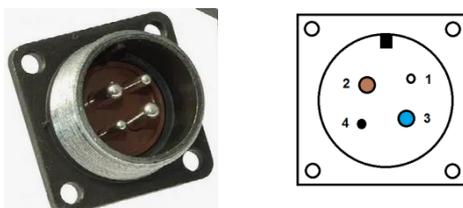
Вилка 2PM22Б4ШЗВ1 на корпус и нумерация выводов (вид на контакты спереди)
